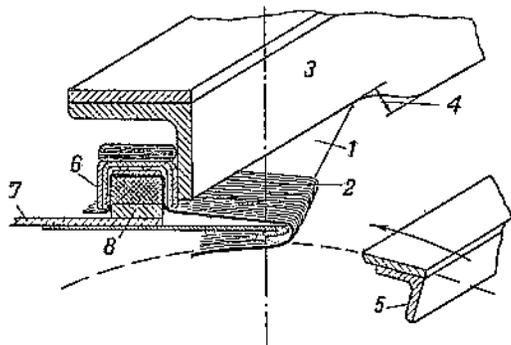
Схема устройства неподвижного козырька ЛТ-6 (общий вид):
